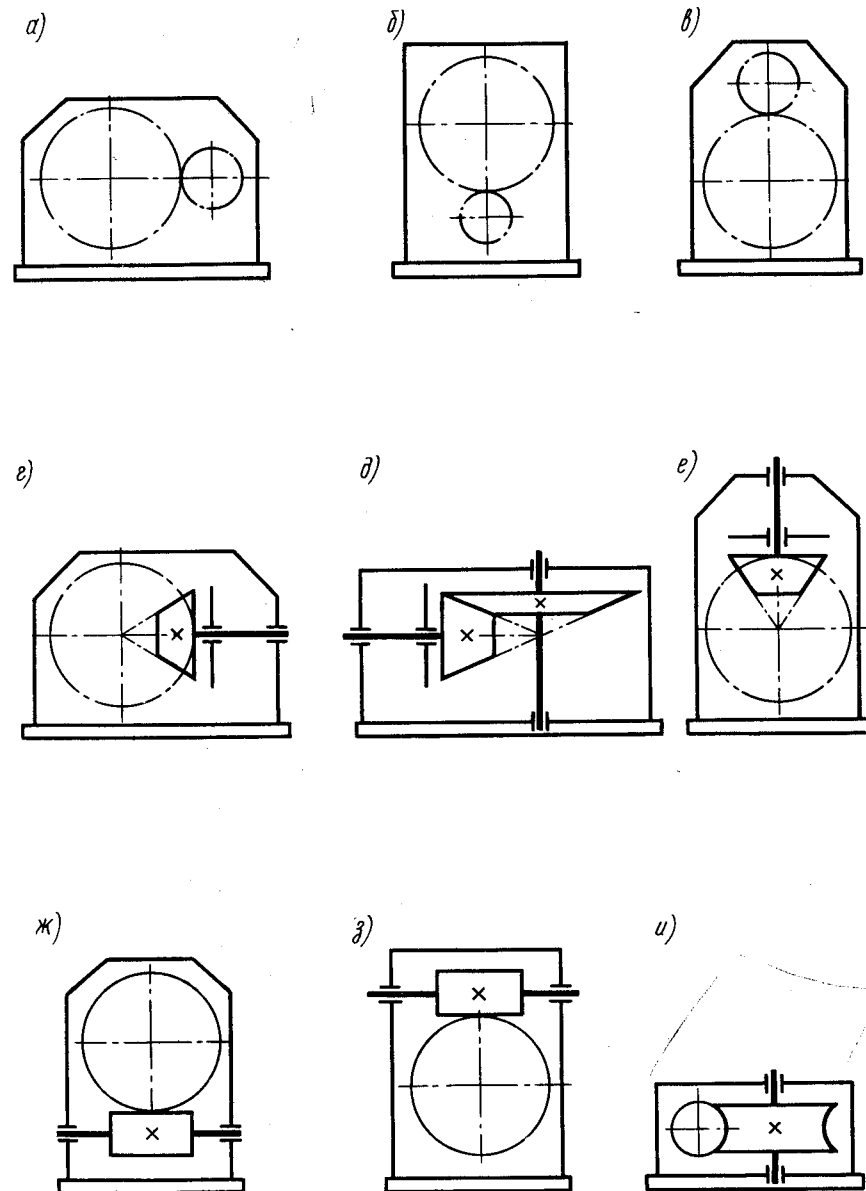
Кинематические схемы одноступенчатых редукторов.
